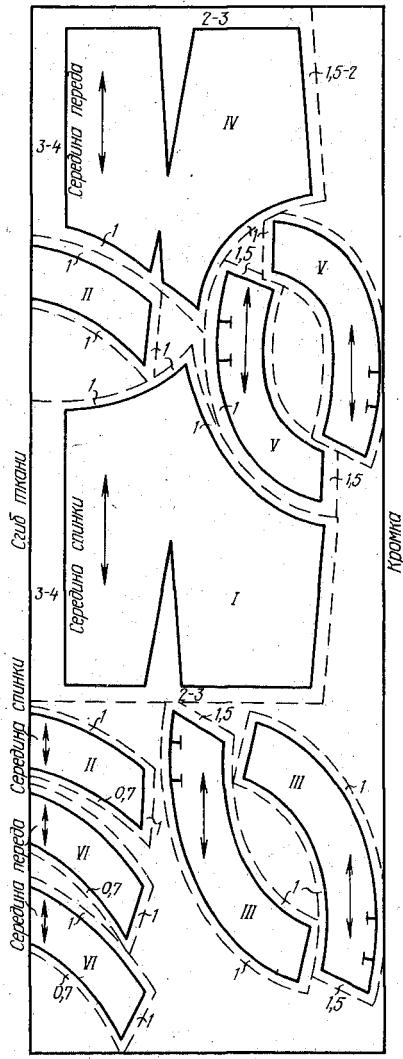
Раскладка выкроек на ткани и раскрой платья-сарафана
